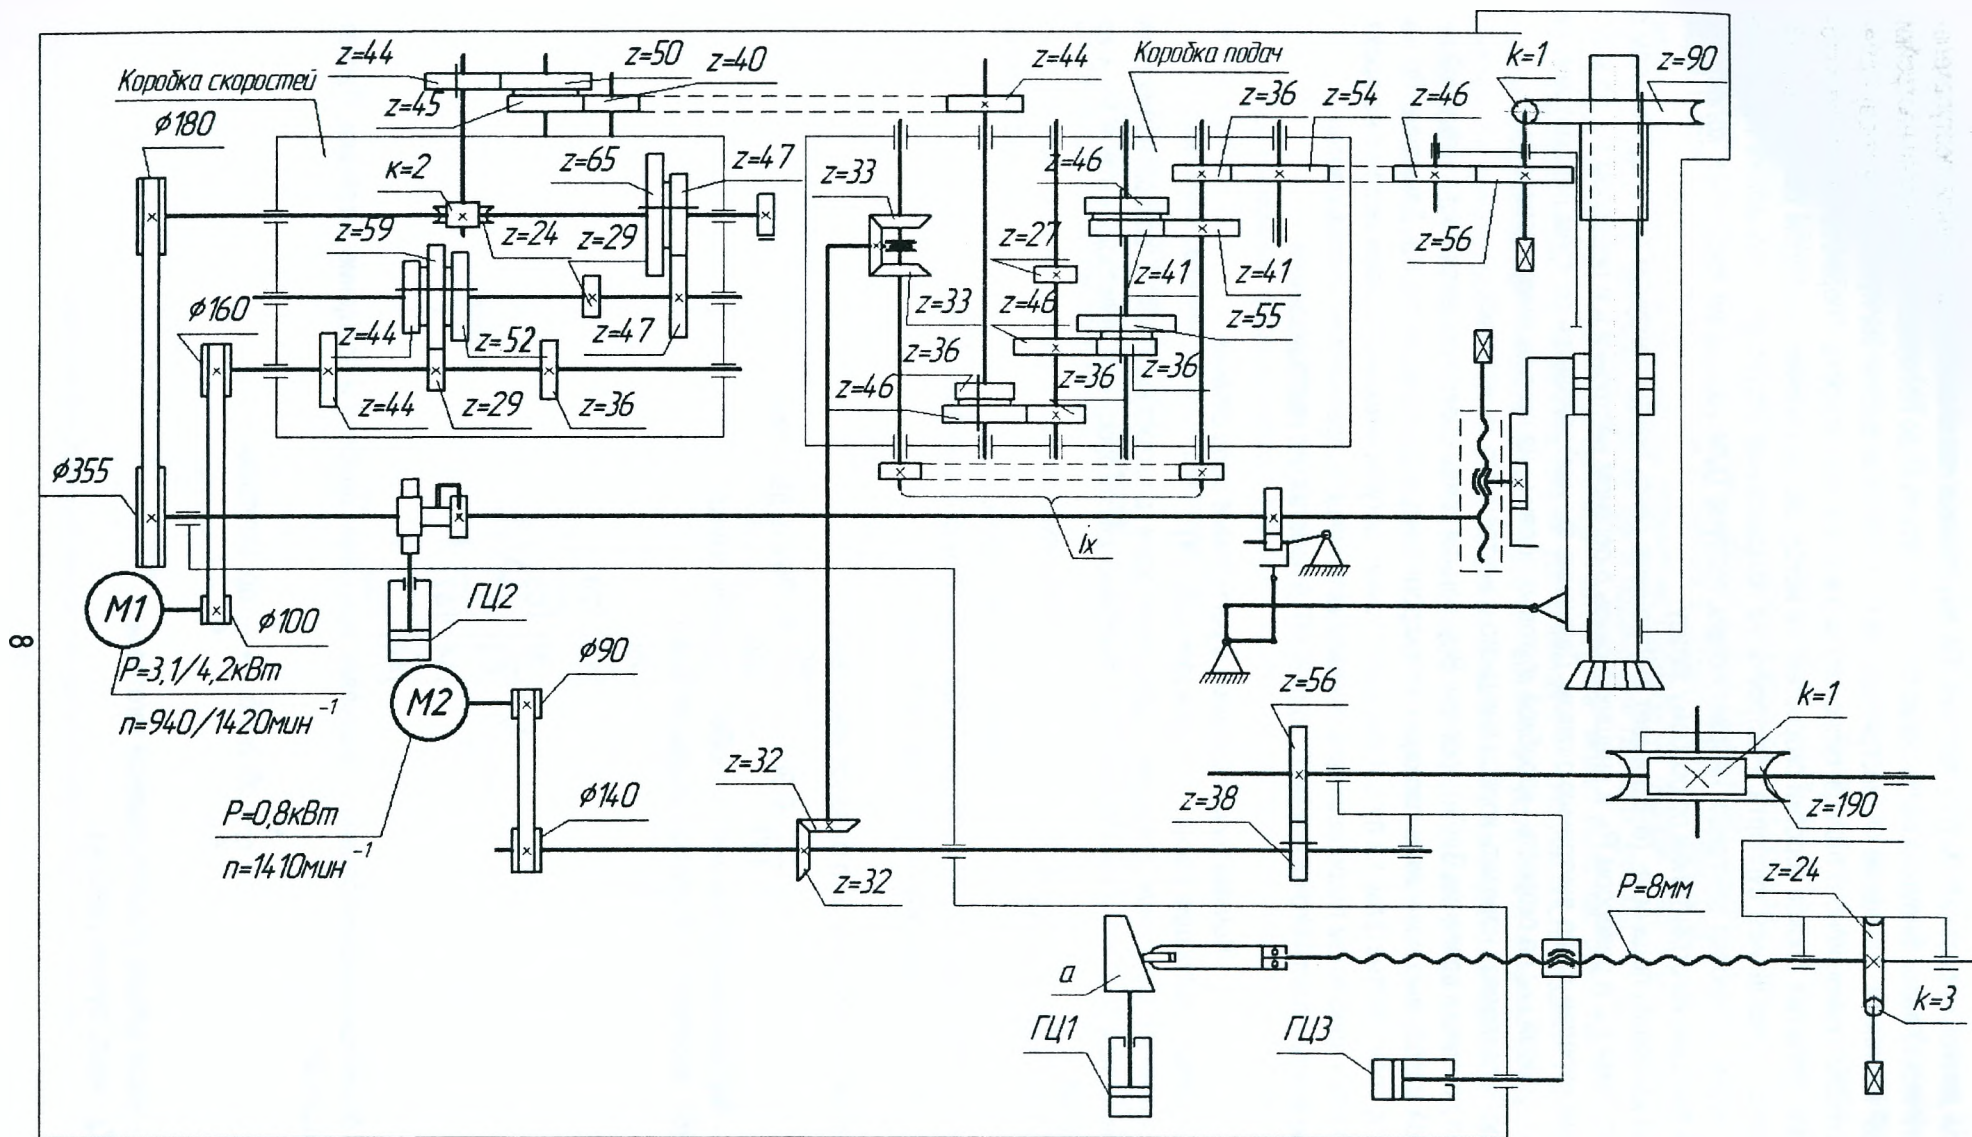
Кинематическая схема зубодолбёжного станка 5140
